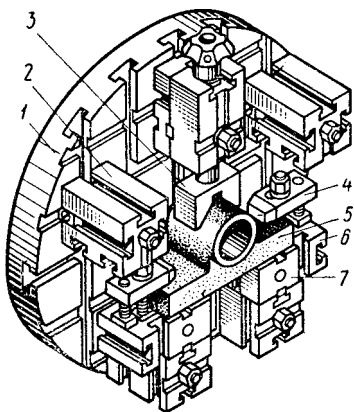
Приспособление системы УСП для токарной обработки корпуса подшипника
